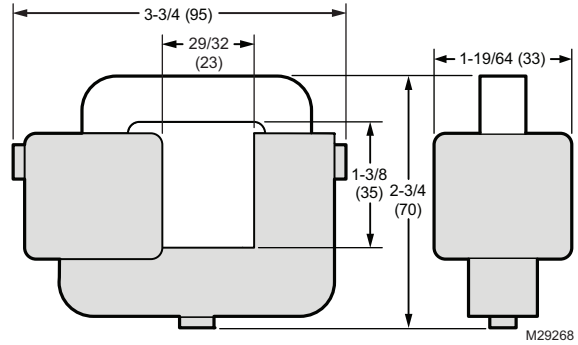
Dimensions du capteur de courant 100 et 200 A en po (mm).
